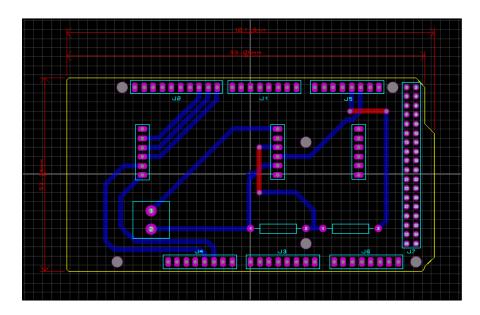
Diseño de shield PCB para el arduino MEGA 2560
